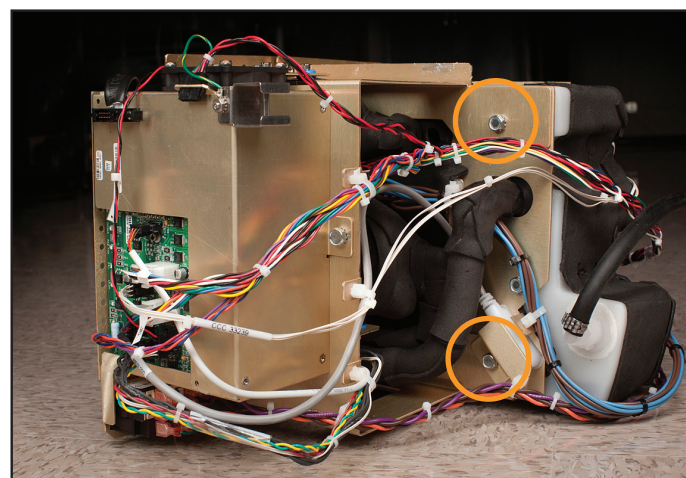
Interne komponenter (set bagfra); cirkler viser bolte, der skal fjernes (trin 1)
